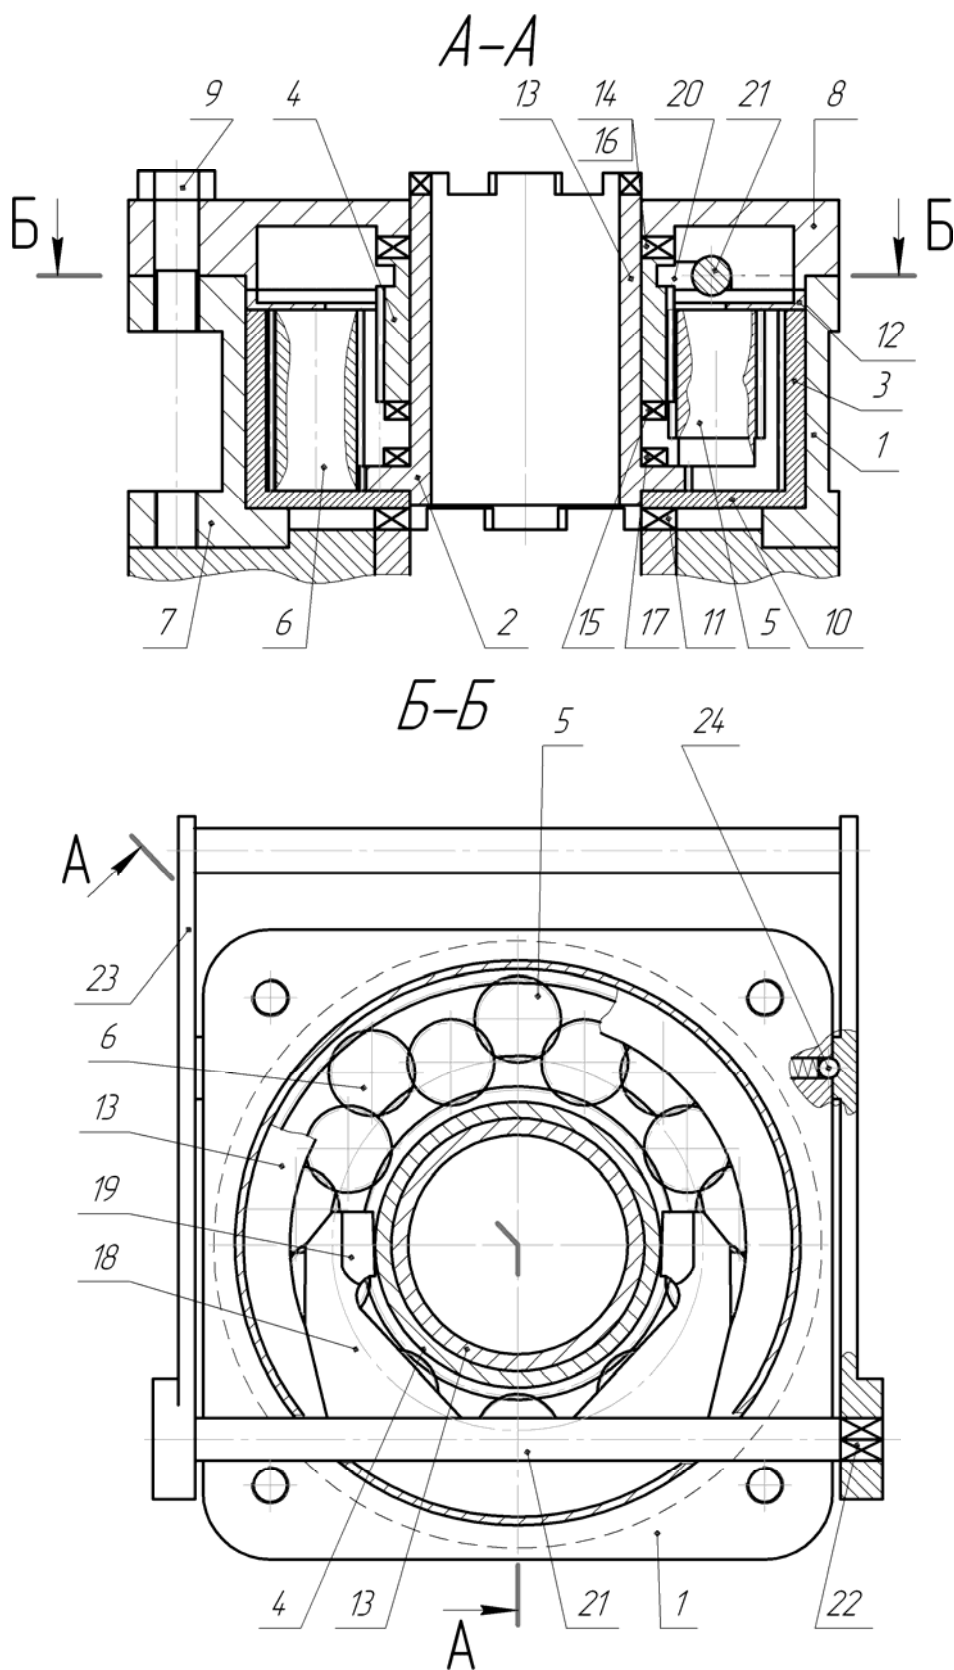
Двухскоростное приводное устройство (RU 108540, Г.Ю. Волков)
